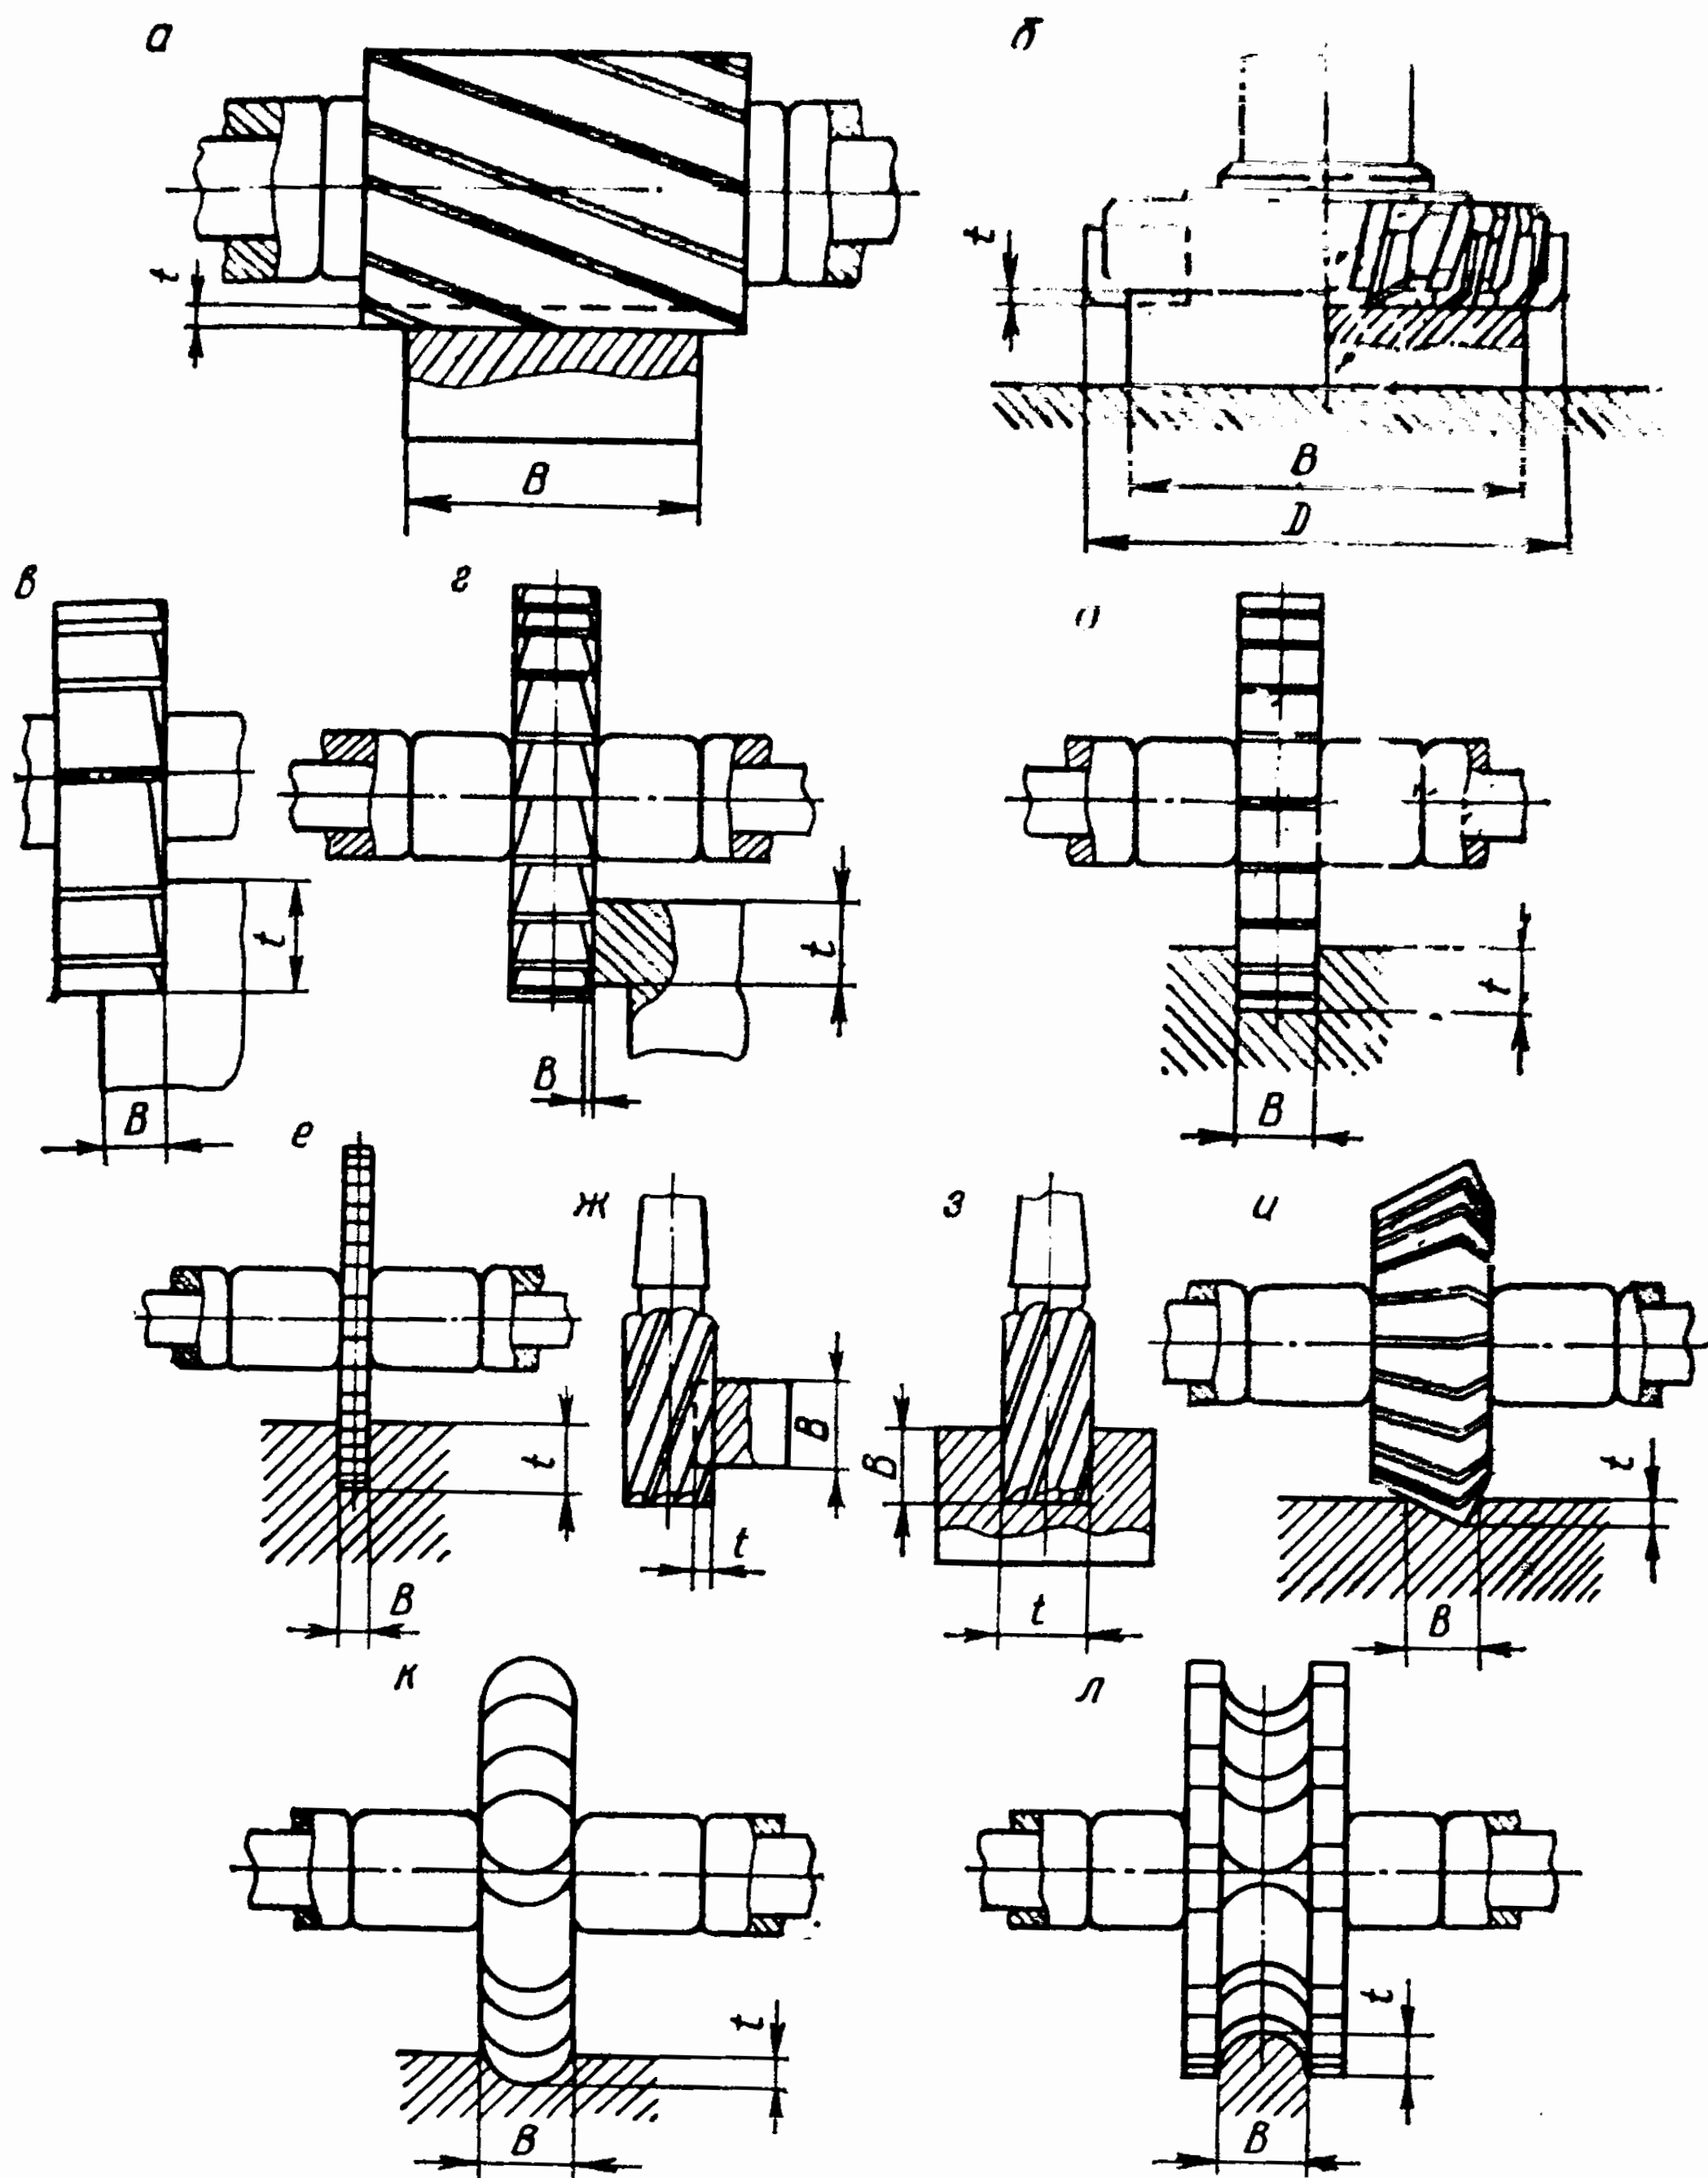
Типы фрез и обрабатываемые ими поверхности.
